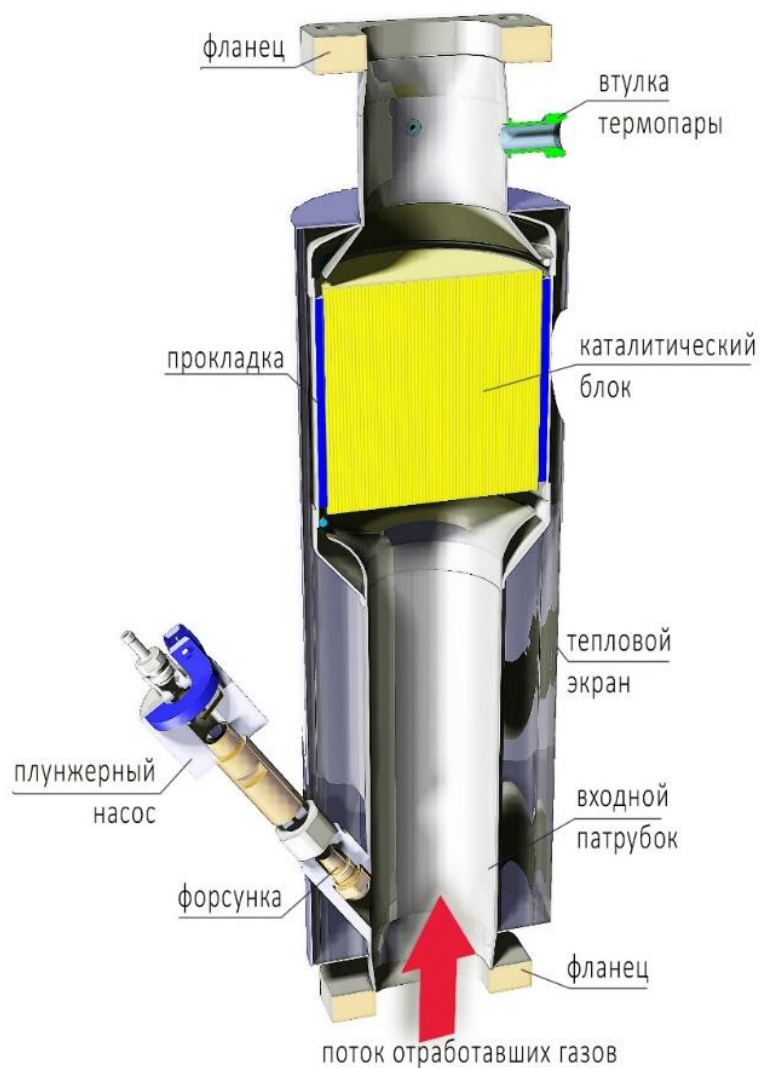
Устройство опытного образца нейтрализатора РТС
